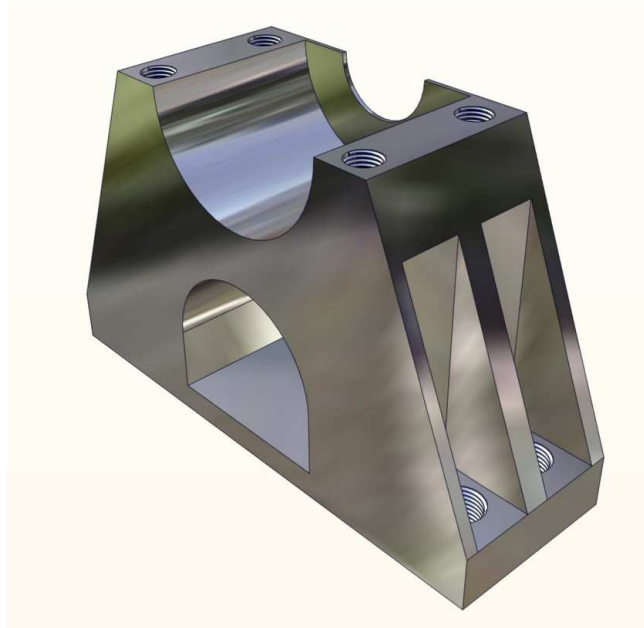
3D модель нижньої частини корпусу.
